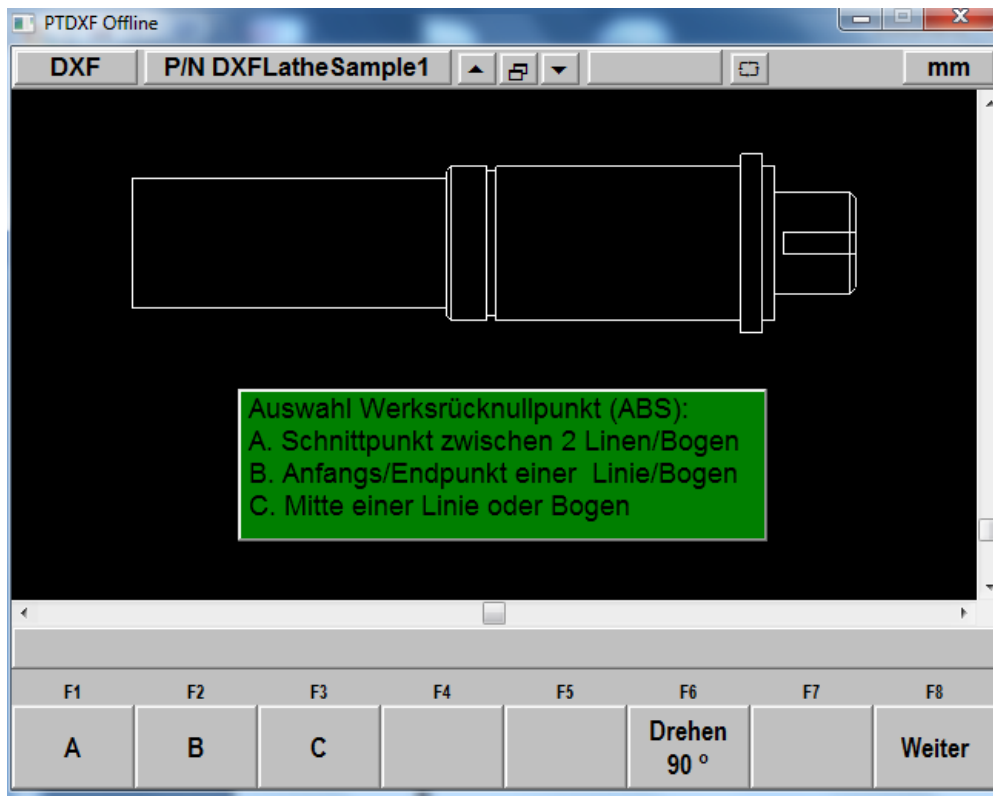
Das Drehteil wurde in die richtige horizontale Position gebracht.
